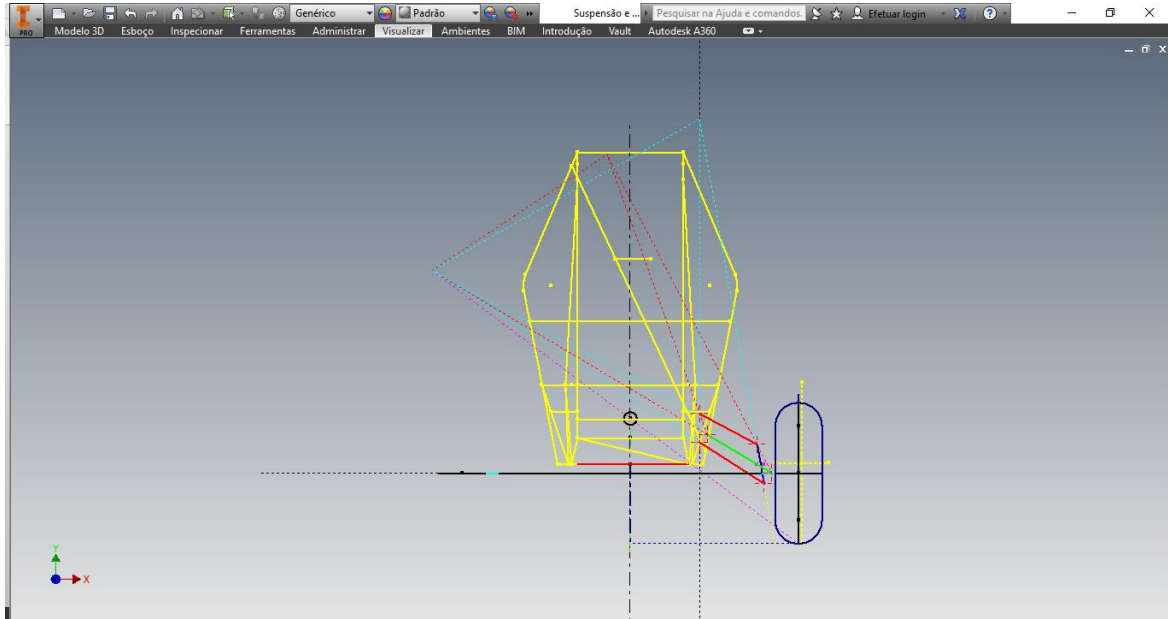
Vista frontal do protótipo com as restrições geométricas.
